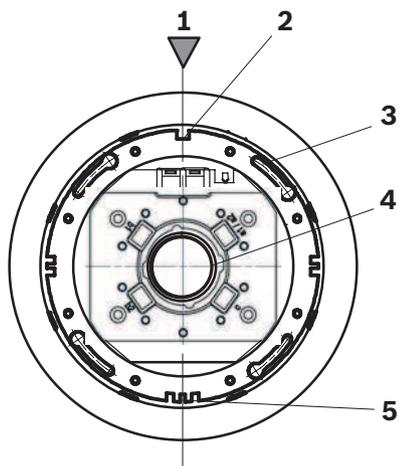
Fixation du socle au boîtier arrière pour montage au plafond
